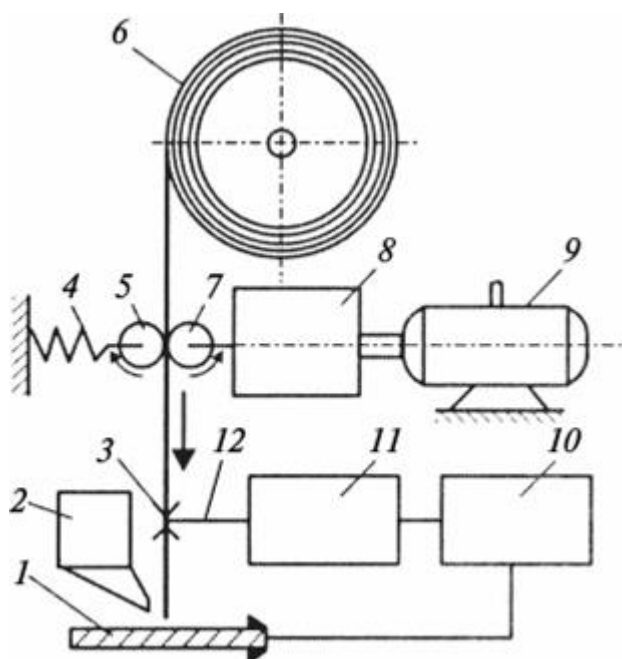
Схема автоматической сварочной головки:
